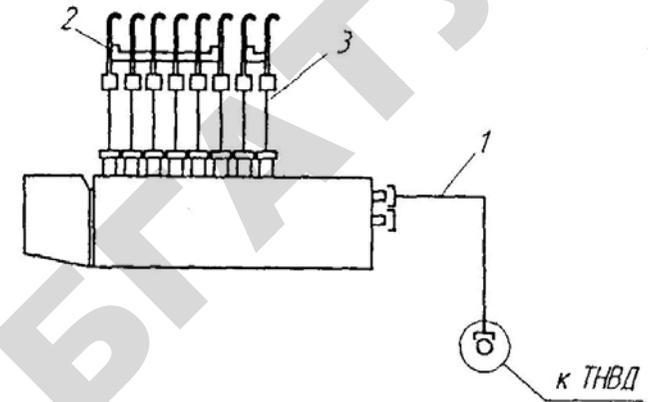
Схема соединения топливопроводов при испытании ТНВД методом пролива:
